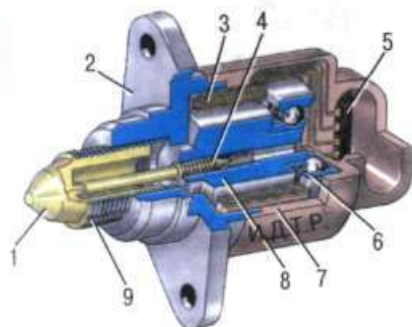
Регулятор холостого хода: 1 – клапан; 2 – корпус регулятора; 3 – обмотка статора; 4 – ходовой винт; 5 – штекерный вывод обмотки статора; 6 – шариковый подшипник; 7 – корпус обмотки статора; 8 – ротор; 9 – пружина
